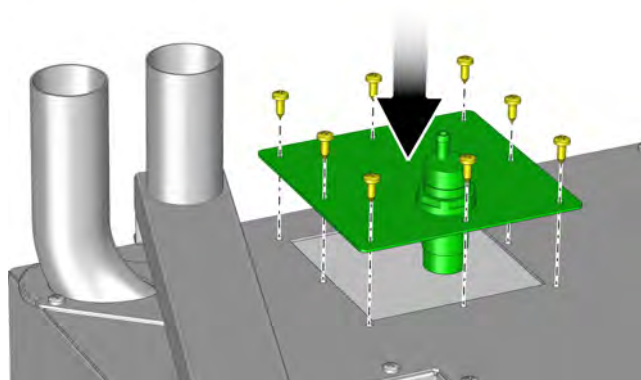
Chapa de montagem do sensor do nível de enchimento
